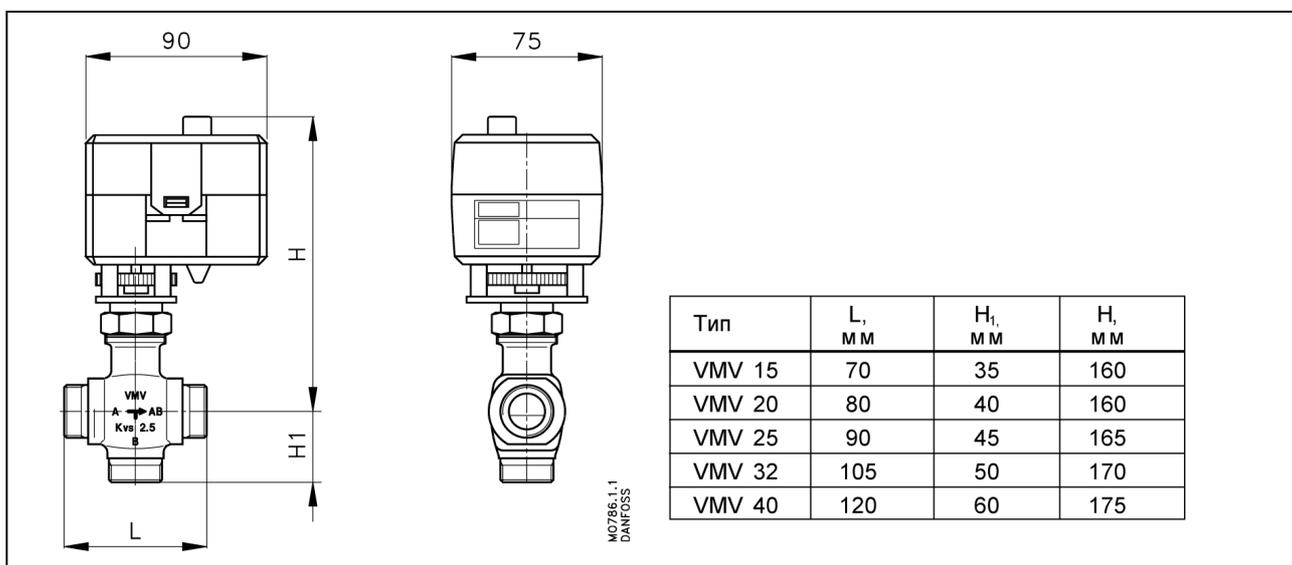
Габаритные и присоединительные размеры AMV 100 с клапаном VMV.
